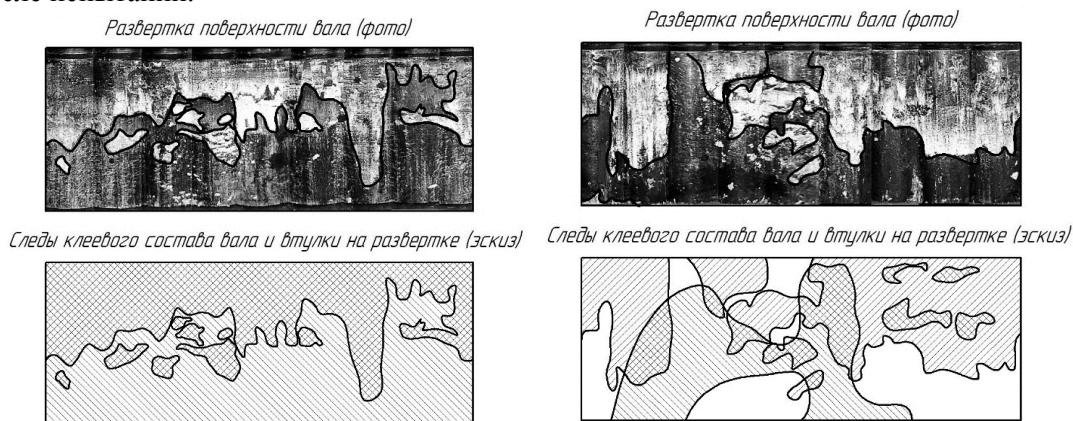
Развертки клеевых соединений (Efele 124, слева – сборка с направленным формированием, справа – ручная сборка)
